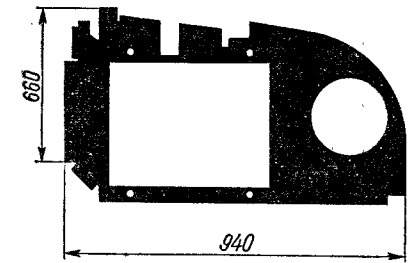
Пример детали, изготовленной на копировально-прорезном прессе
